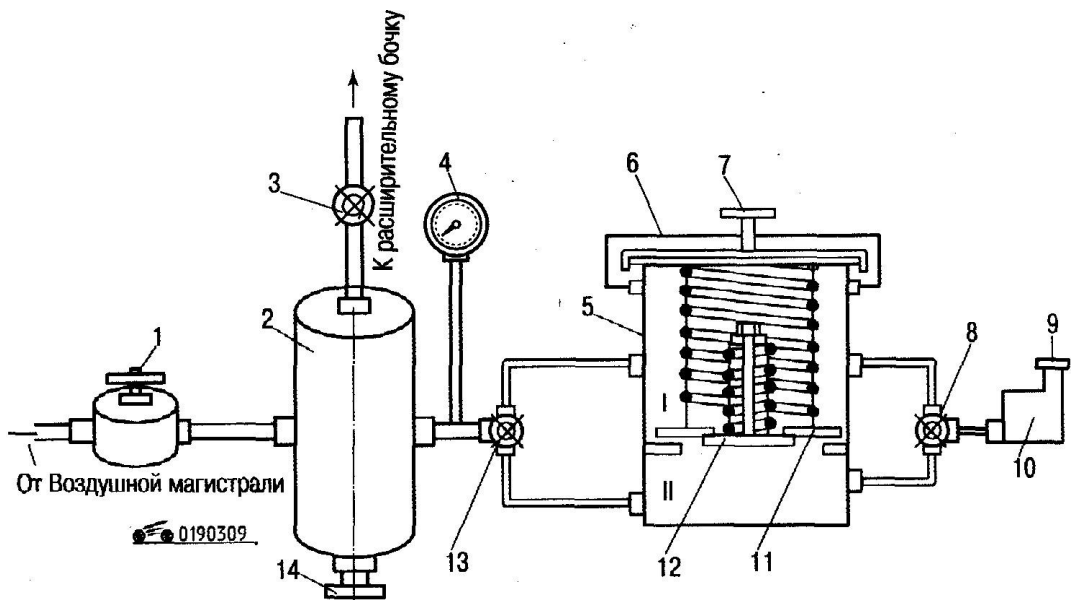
Схема приспособления для проверки клапанов пробки расширительного бачка и герметичности системы охлаждения дизеля: 1 - редуктор; 2 - баллон; 3 - кран; 4 - манометр; 5 - стакан; 6 - рамка; 7 - зажим; 8, 13 -
